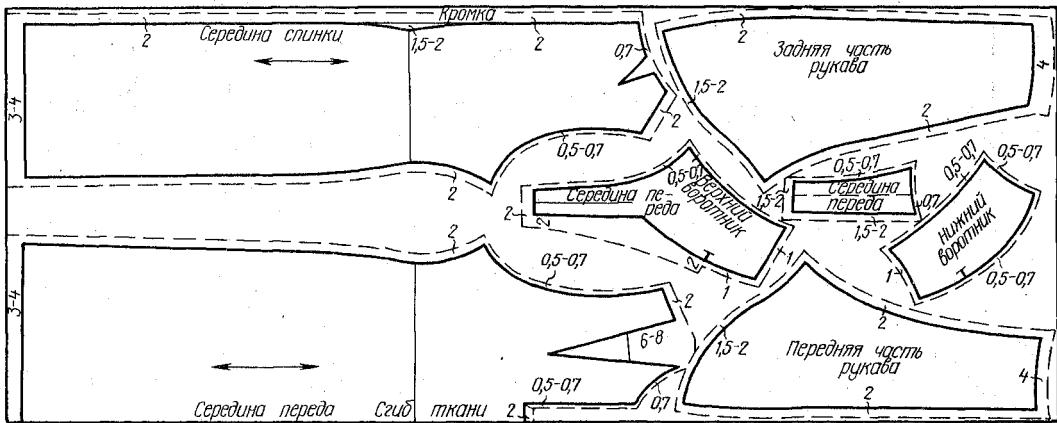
Раскладка выкроек на ткани и раскрой платья с кантами
